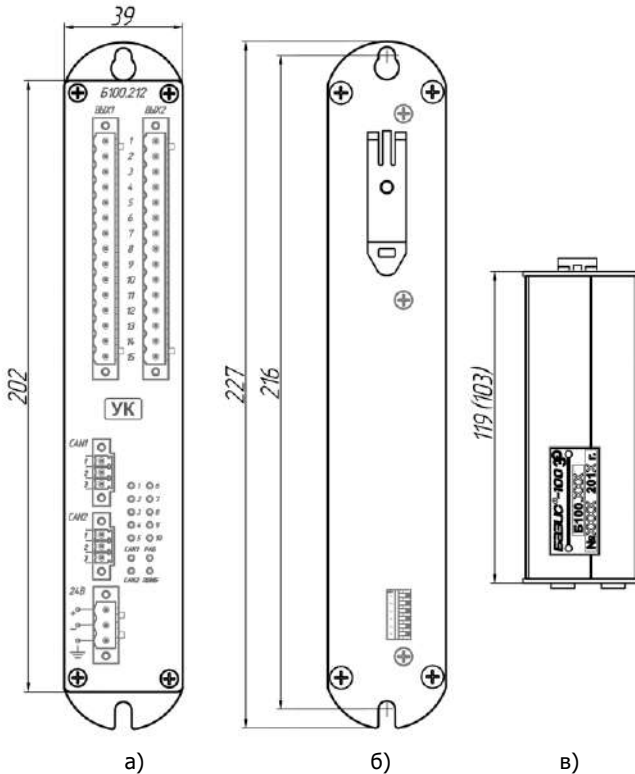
Вид корпуса Ш2 модуля Контроллера:
